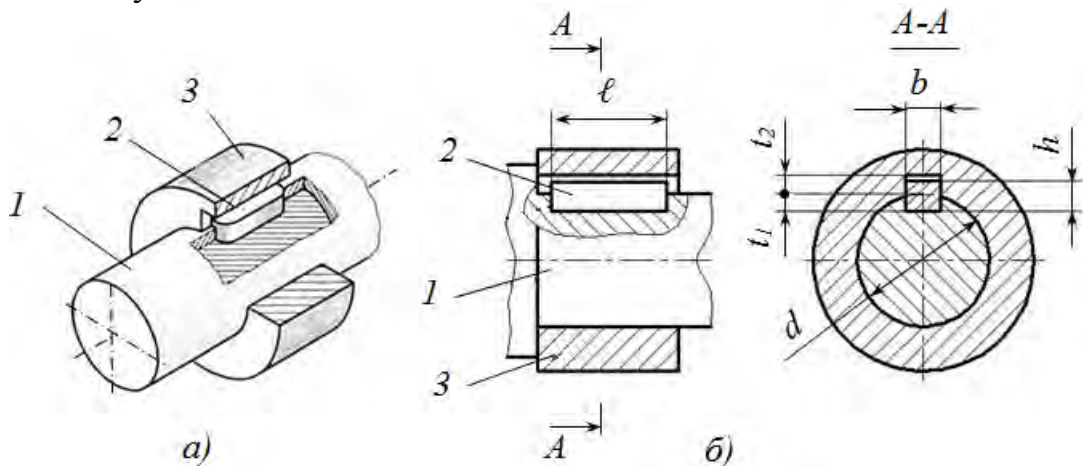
Загальний вигляд (а) та креслення шпонкового з'єднання (б):
